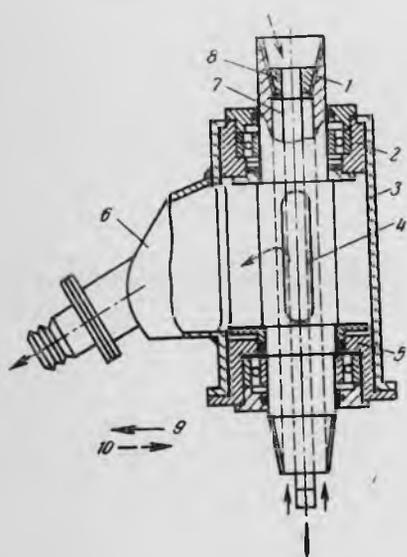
Вертлюжная приставка для установок УРБ-ЗАМ и БА-15В:
